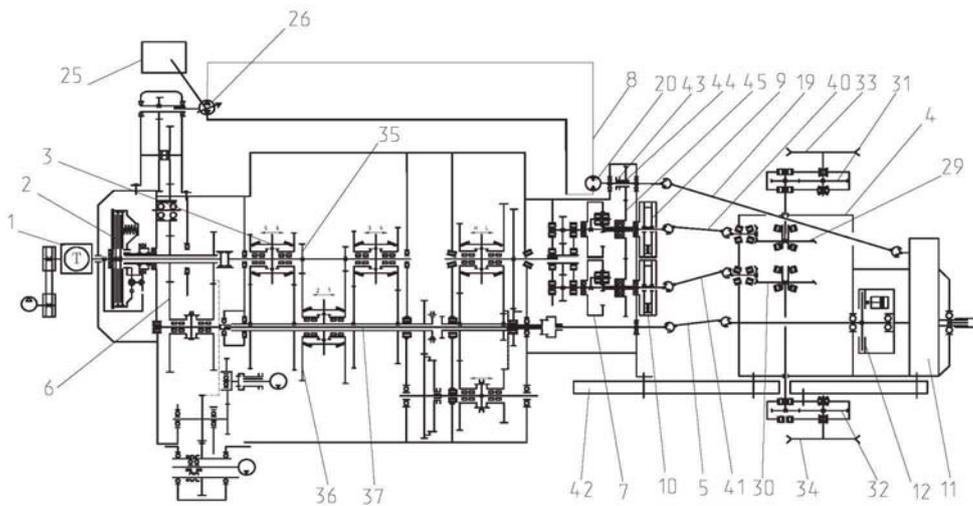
Кинематическая схема привода вала отбора мощности и ходовой системы гусеничного трактора
